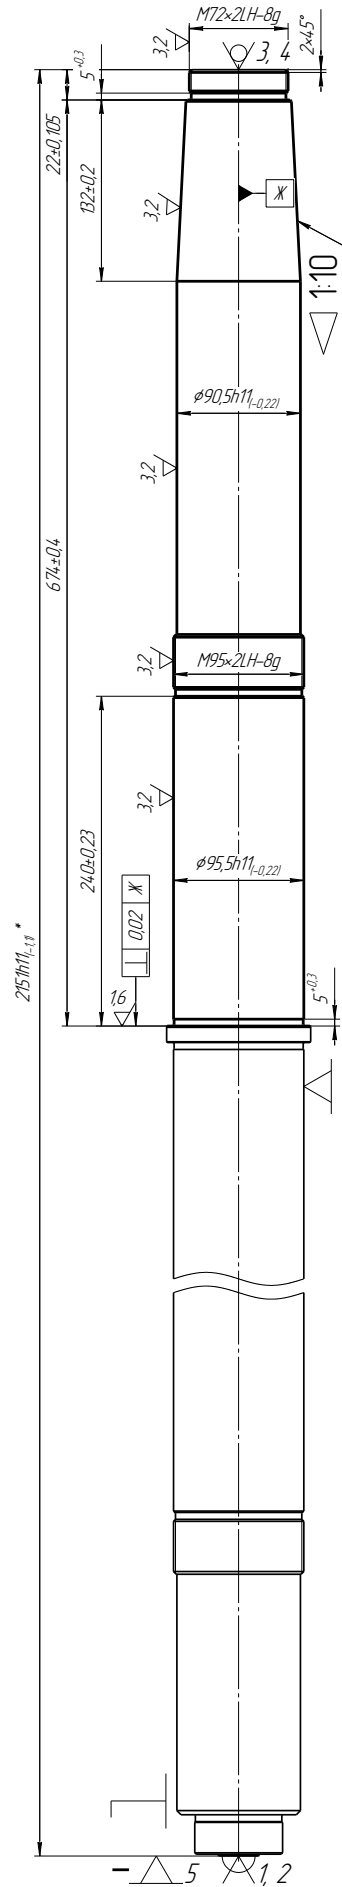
Схема установки заготовки на плавающий и вращающийся центра
